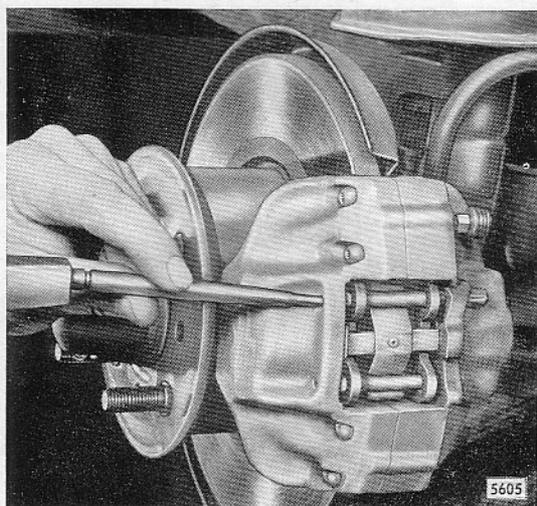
Haltestifte für Bremsbeläge aus Bremssattel herausschlagen
